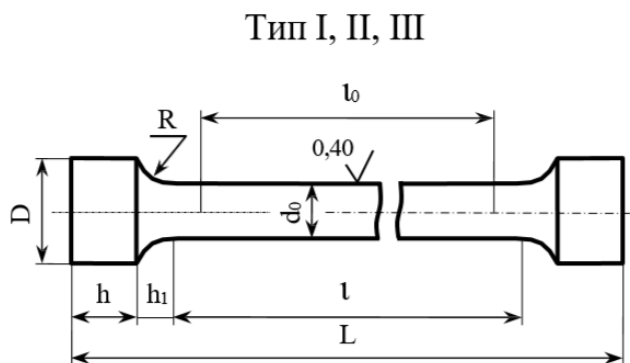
Геометрические параметры стандартных круглых образцов типов I, II, III по ГОСТ 6996 для испытаний на статическое растяжение металла шва сварного соединения
